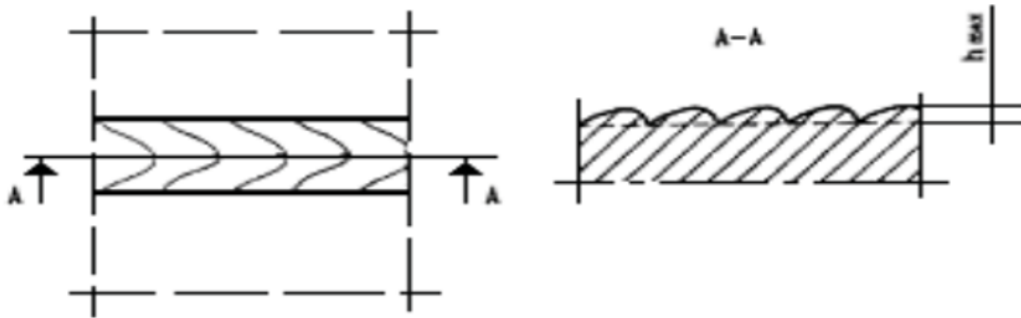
Эскиз дефекта сварного шва
